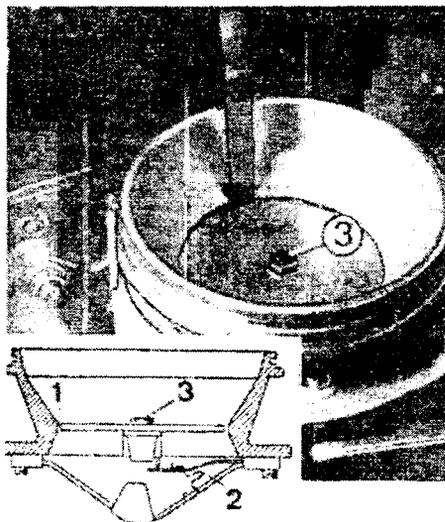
Регулировка положения напорного диска расходомера воздуха:
